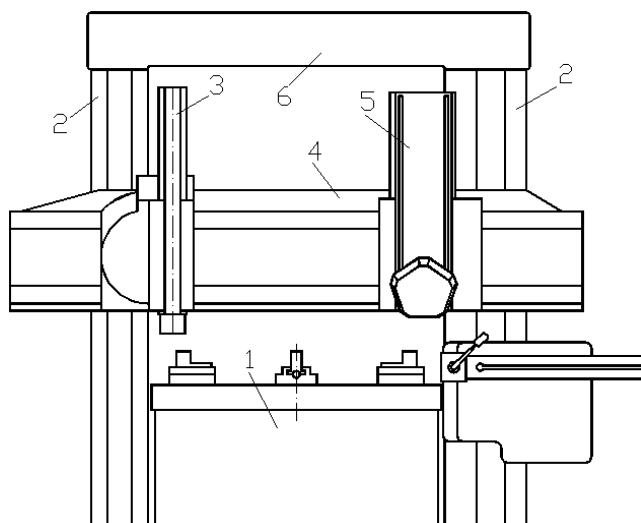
Общий вид двухстоечного токарно-карусельного станка
